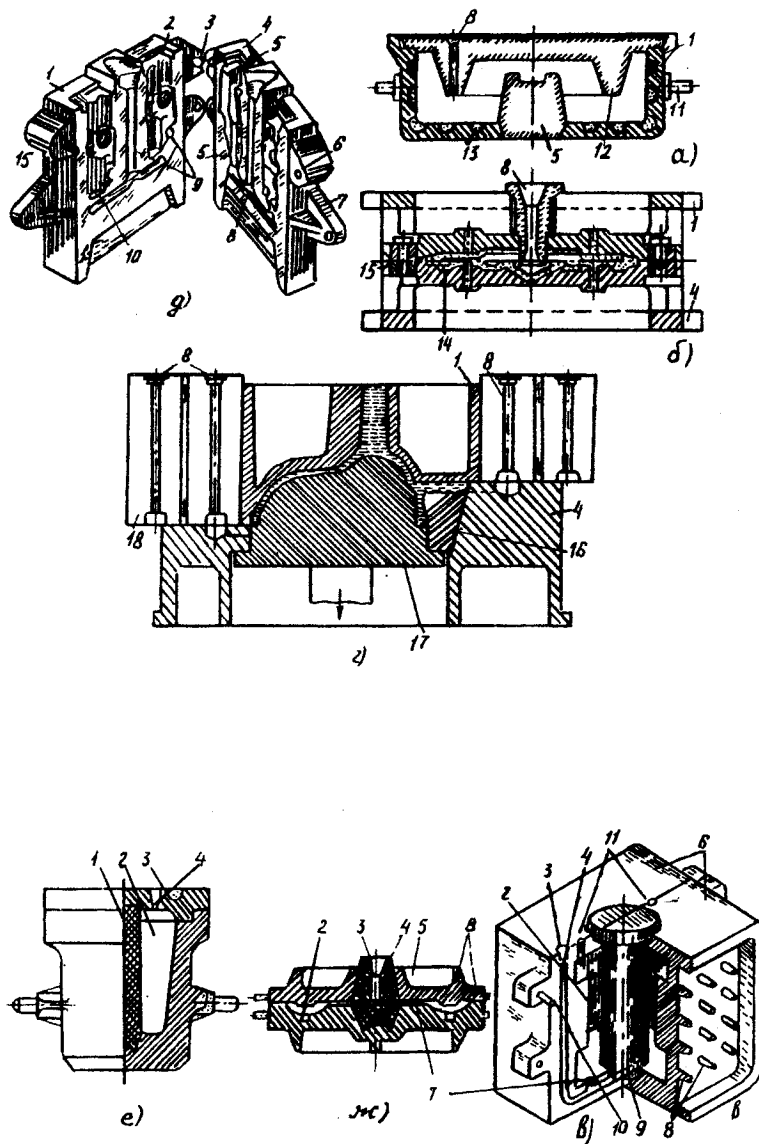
Приклади виготовлення виливків в кокілях (металічних моделях)
